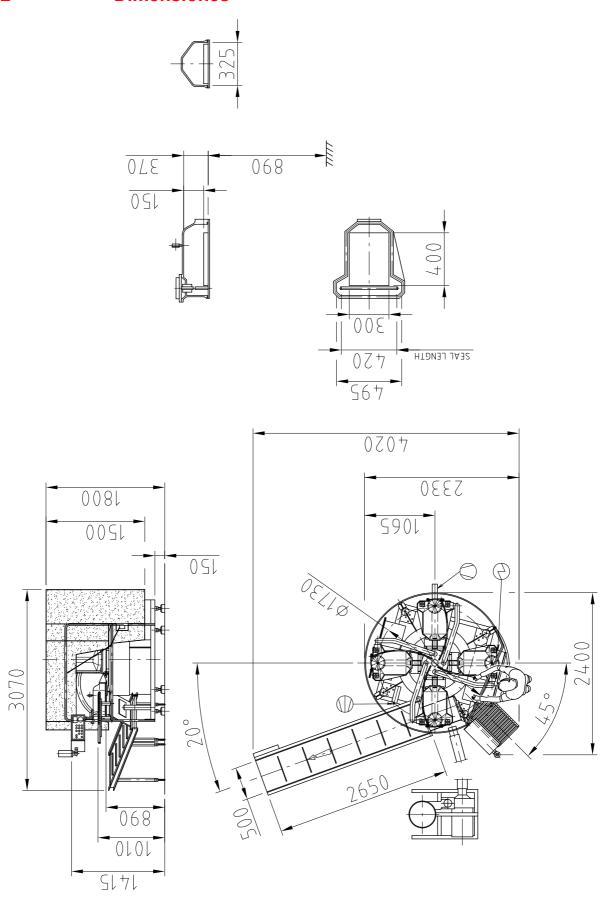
, Dimensiones LR (flujo del producto de izquierda a derecha)
